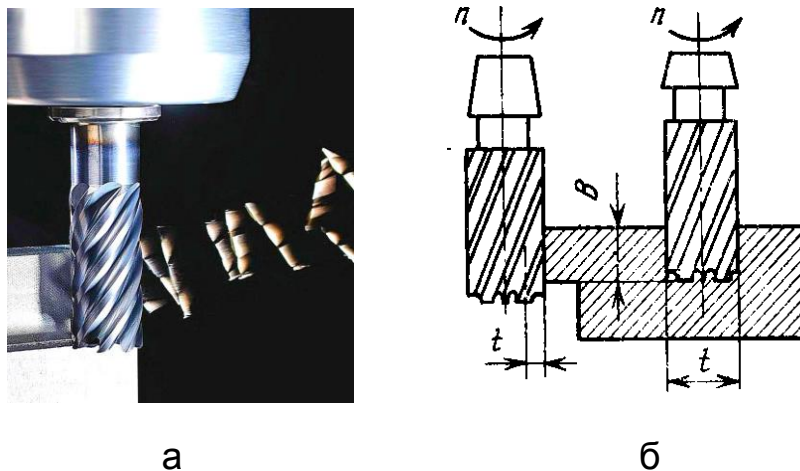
Глибина і ширина фрезерування для кінцевої фрези
